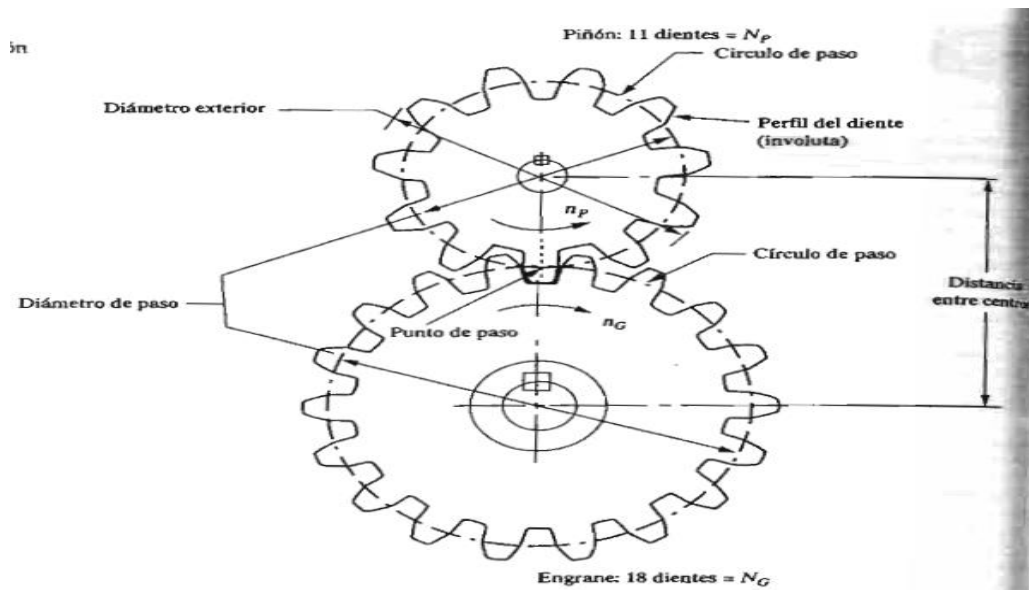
Par de engranajes rectos. El piñón impulsa al engranaje, (Robert L. Mott, 2006)
